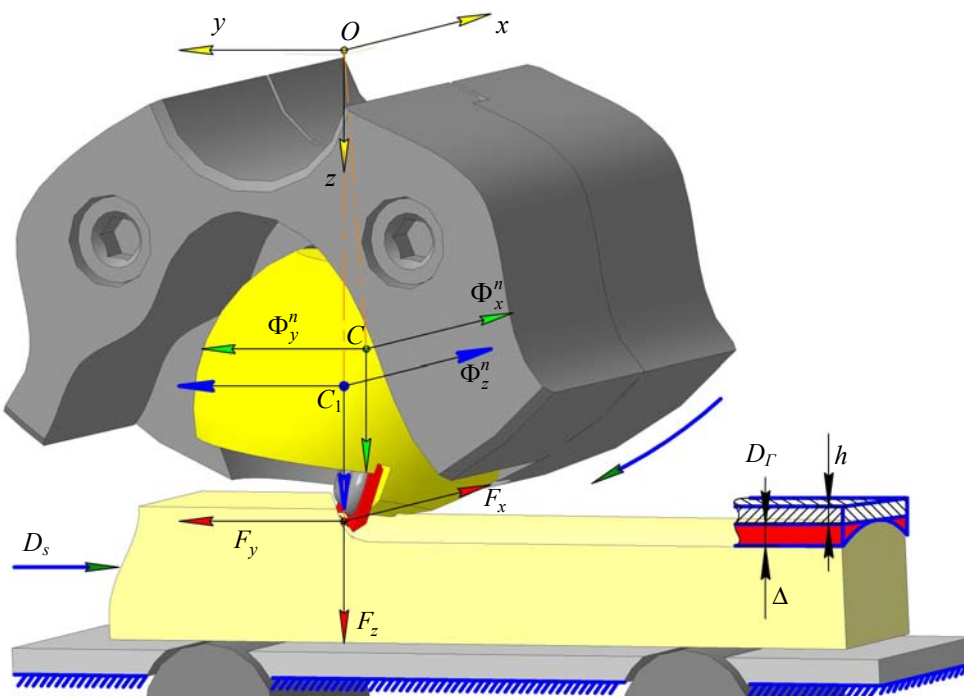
Расчетная схема фрезы в режиме обработки материала
